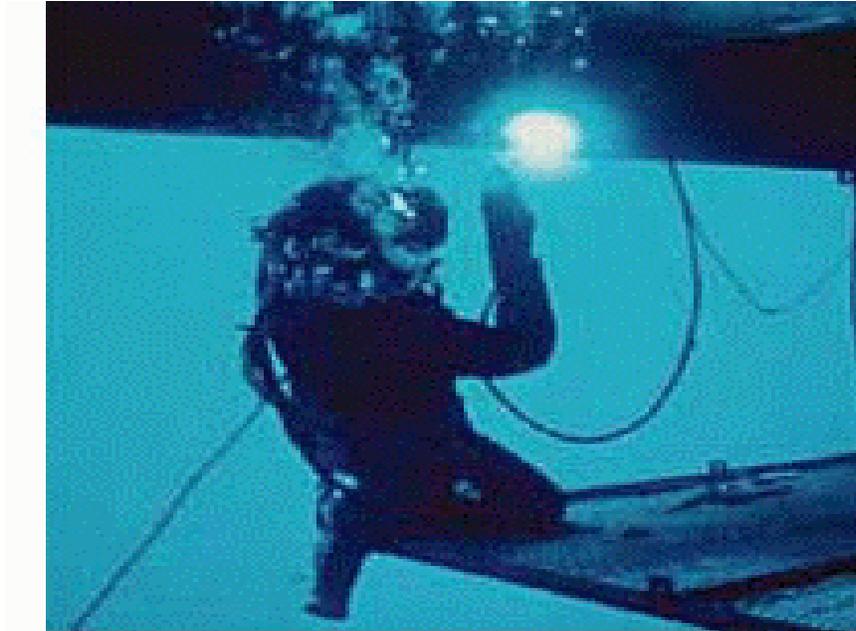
Andamios y soporte en operaciones de corte y soldadura.
